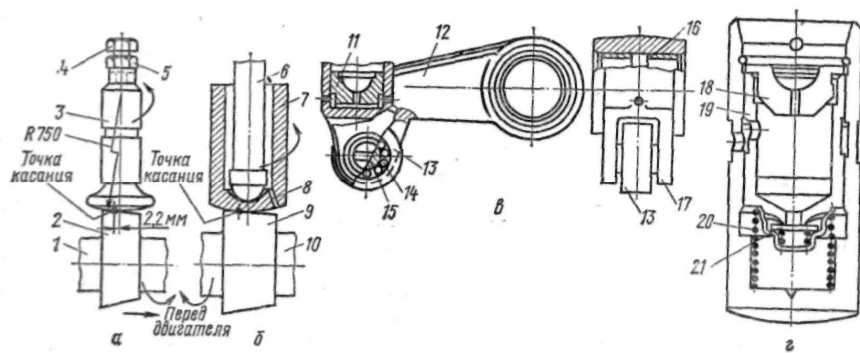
Конструктивні схеми штовхачів: а і б – грибоподібний і циліндричний зі сферичними опорними поверхнями; в – роликовий; з – гідравлічний; 1 і 10 – розподільчі вали; 2 і 9 – кулачки; 3, 7 і 12 – штовхачі; 4 – регулювальний болт; 5 – контргайка; 5 – штанга; 8 – отвір для стікання мастила; 11 – п'ята; 13 – ролик; 14 – голковий підшипник; 15 – вісь ролика; 16 – втулка; 17 – вилка штовхача; 18 – сферична опора; 19 – стакан; 20 – пружина; 21 – плоский клапан
